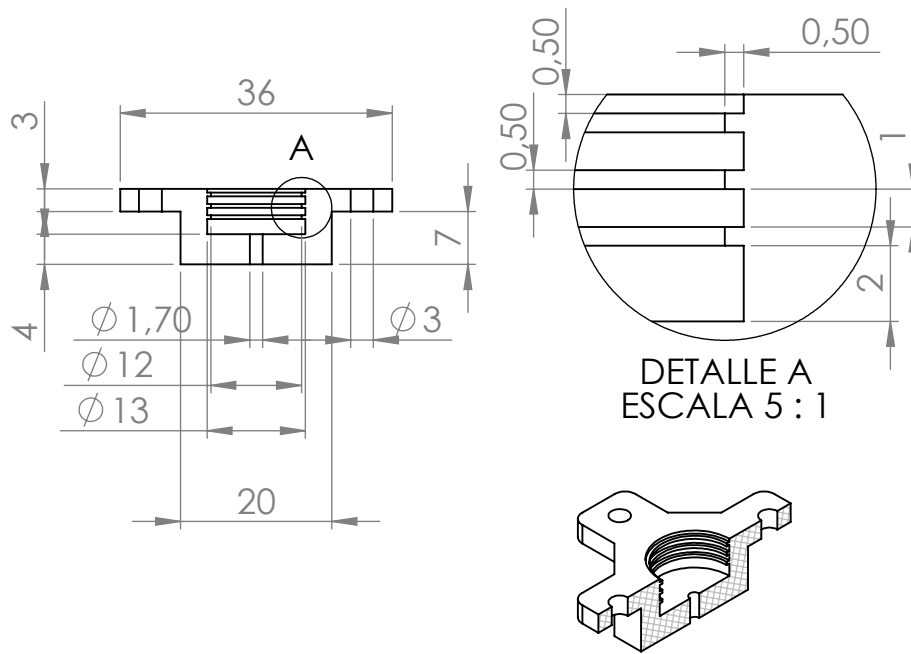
Vista en corte del molde del *Robot Shear* parte A
